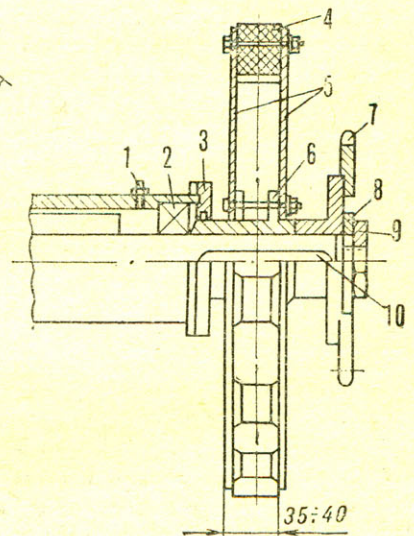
Ведущее колесо ленты: 1 — маслянка, 2 — подшипник, 3 — крышка с сальником, 4 — секция венца, 5 — диски, 6 — ступица, 7 — ведомая звездочка, 8 — шайба, 9 — гайка, 10 — шпонка.
